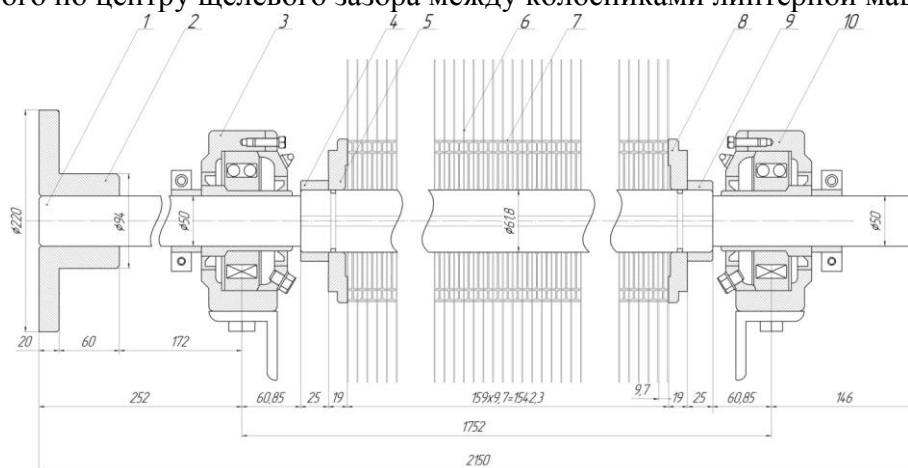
Пильный цилиндр линтерной машины марки 5ЛП: 1 – вал; 2 – полумуфта; 3, 10 – корпус подшипников; 4, 9 – гайки; 5, 8 – шайбы; 6 – пильные диски; 7 – междупильные прокладки
